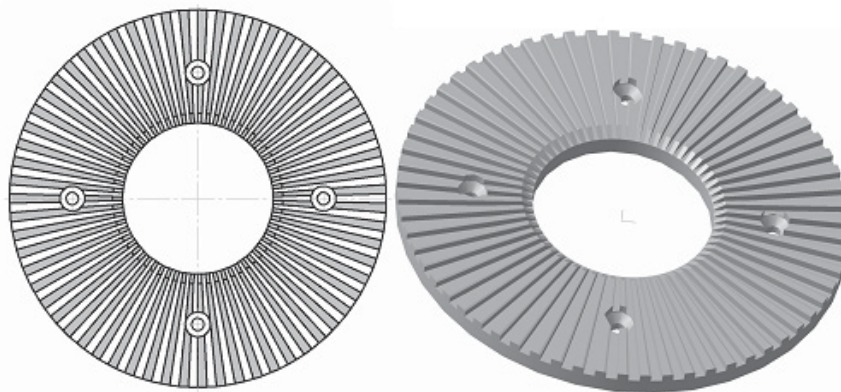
Ножевая гарнитура для размла волокнистых полуфабрикатов с радиальным расположением ножей
